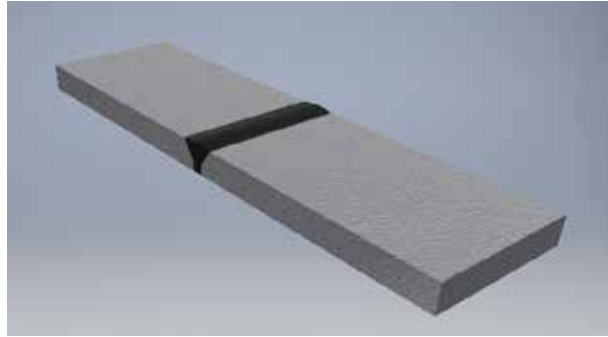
Esquema 3D de la probeta de doblado con el cordón de soldadura utilizando SolidWorks.
